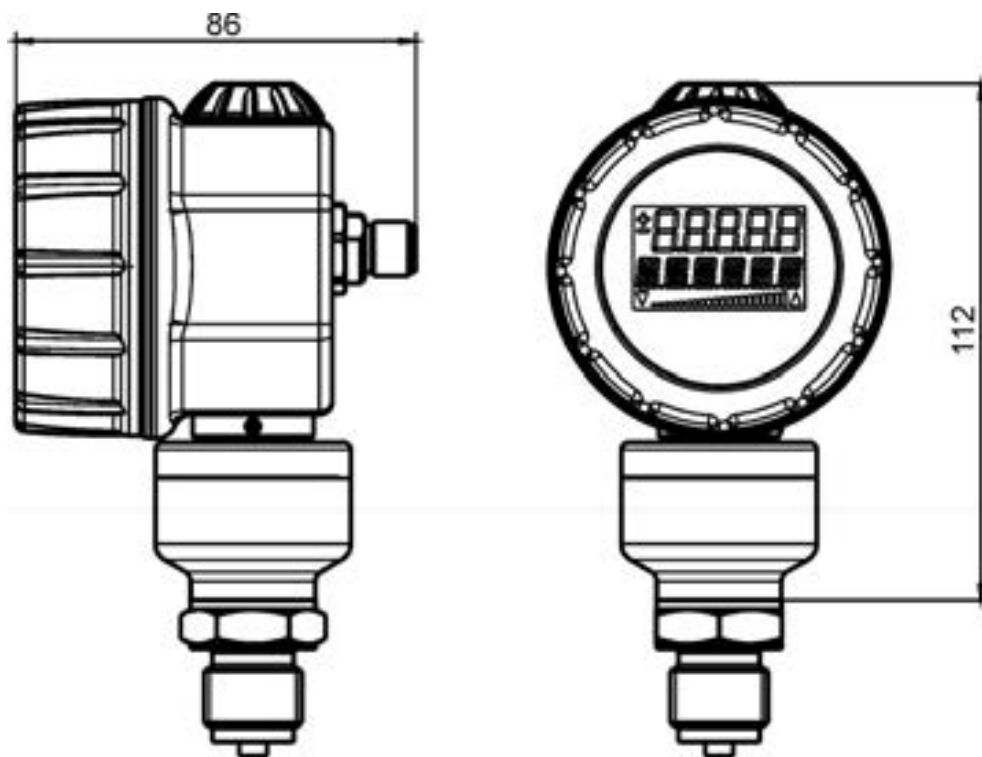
Габаритные размеры преобразователя давления Альбатрос р20 (короткий корпус, нержавеющая сталь, с разъемом М12)
